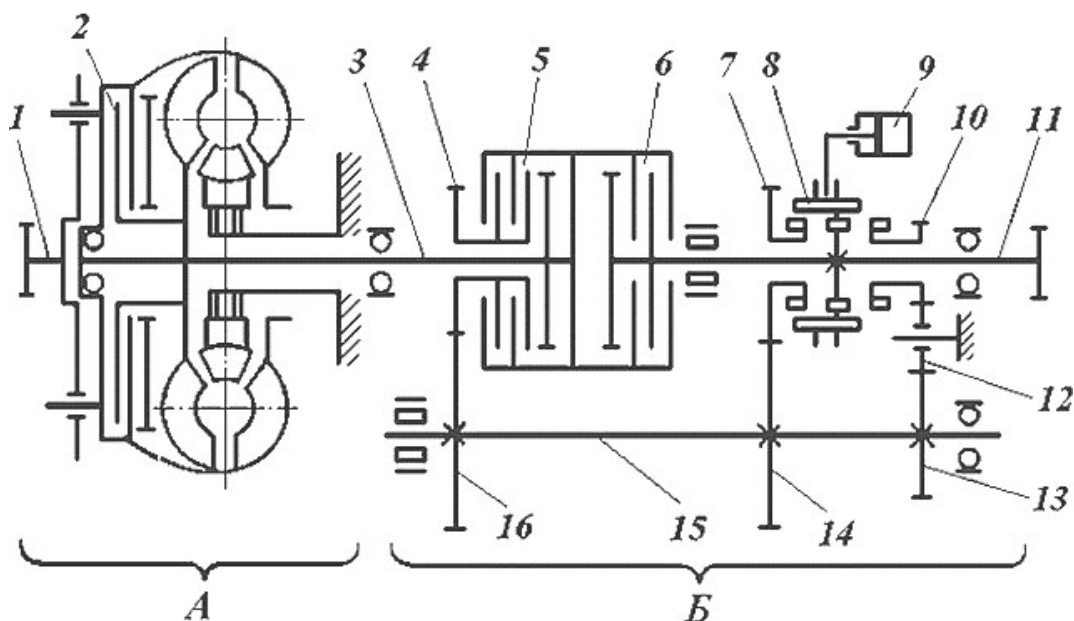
Схема гидромеханической передачи с двухступенчатой коробкой передач:
